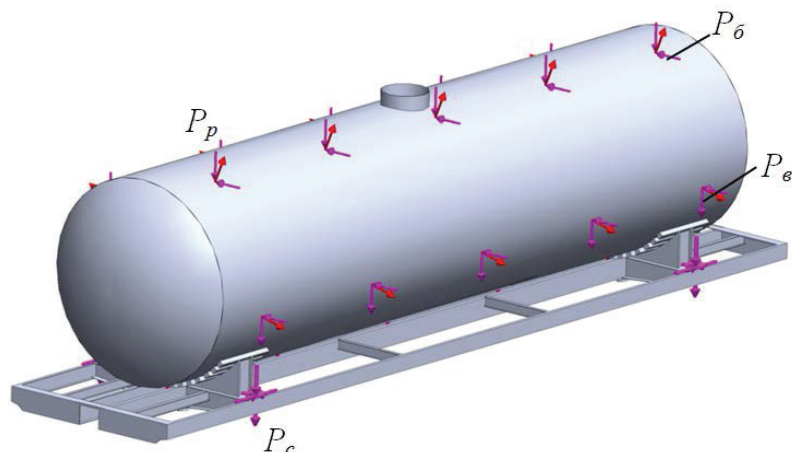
Розрахункова схема несучої конструкції вагона-цистерни
